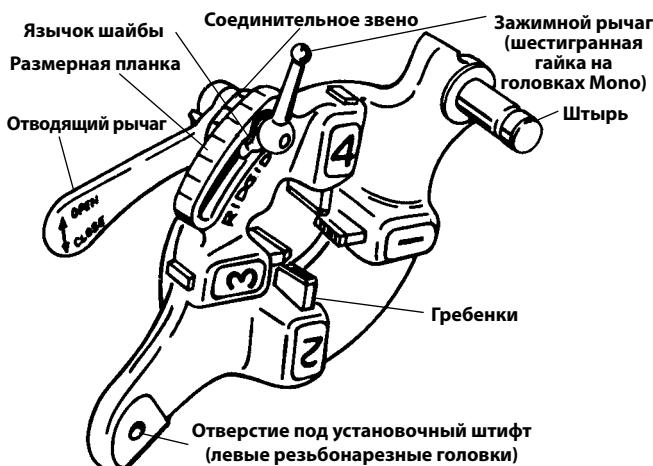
Быстрооткрывающаяся резьбонарезная головка
